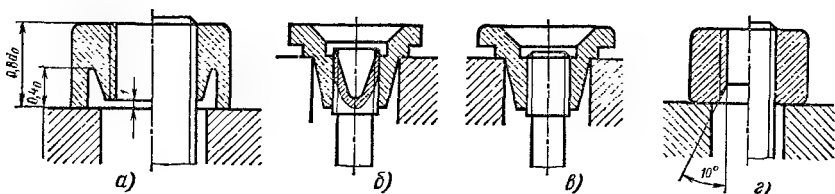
Конструкции гаек для более равномерного распределения нагрузки по виткам резьбы:
